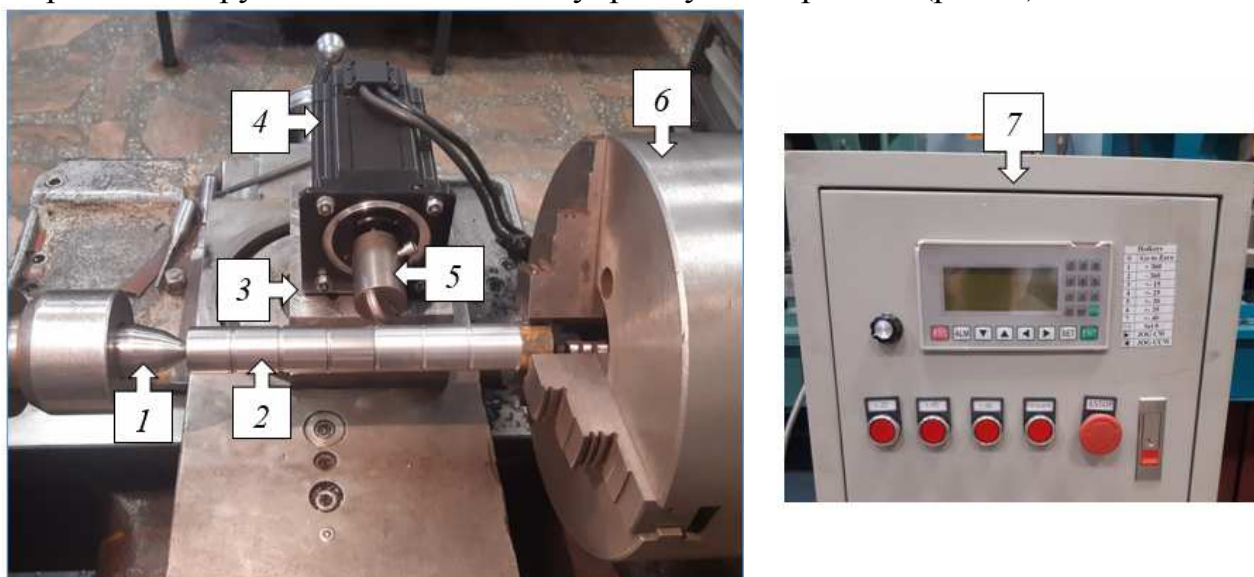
Общий вид устройства для реверсивного выглаживания наружных поверхностей цилиндрических деталей на токарном станке: 1 – задний центр; 2 – обрабатываемый образец; 3 – основание; 4 – шаговый электродвигатель; 5 – рабочий инструмент; 6 – трехкулачковый патрон; 7 – панель управления параметрами движения рабочего инструмента
